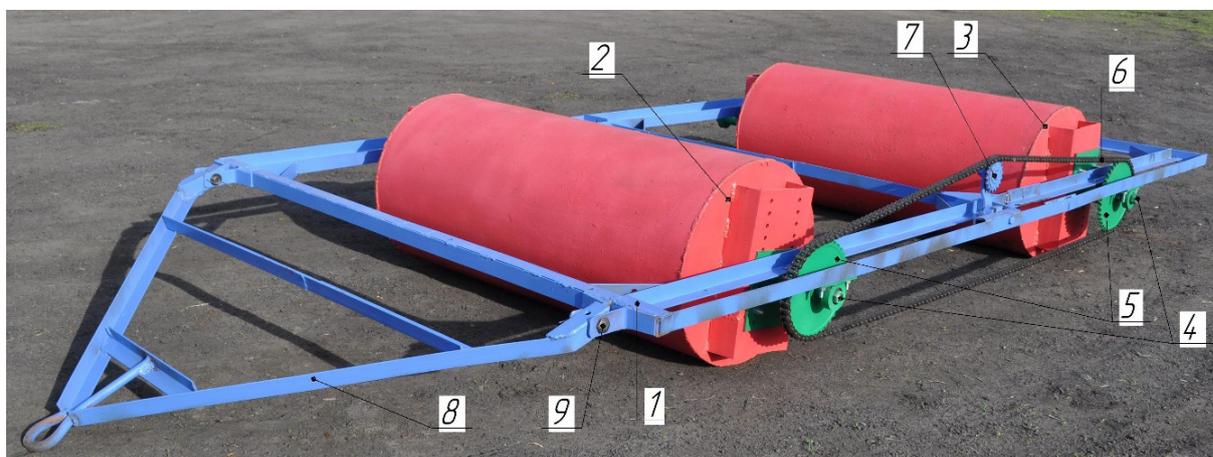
Эксцентриковый почвообрабатывающий каток: 1 – рама; 2, 3 – пустотелые цилиндры; 4 – оси пустотелых цилиндров; 5 – звездочки; 6 – цепь роликовая; 7 – натяжная звездочка; 8 – прицепное устройство; 9 – шарнир
